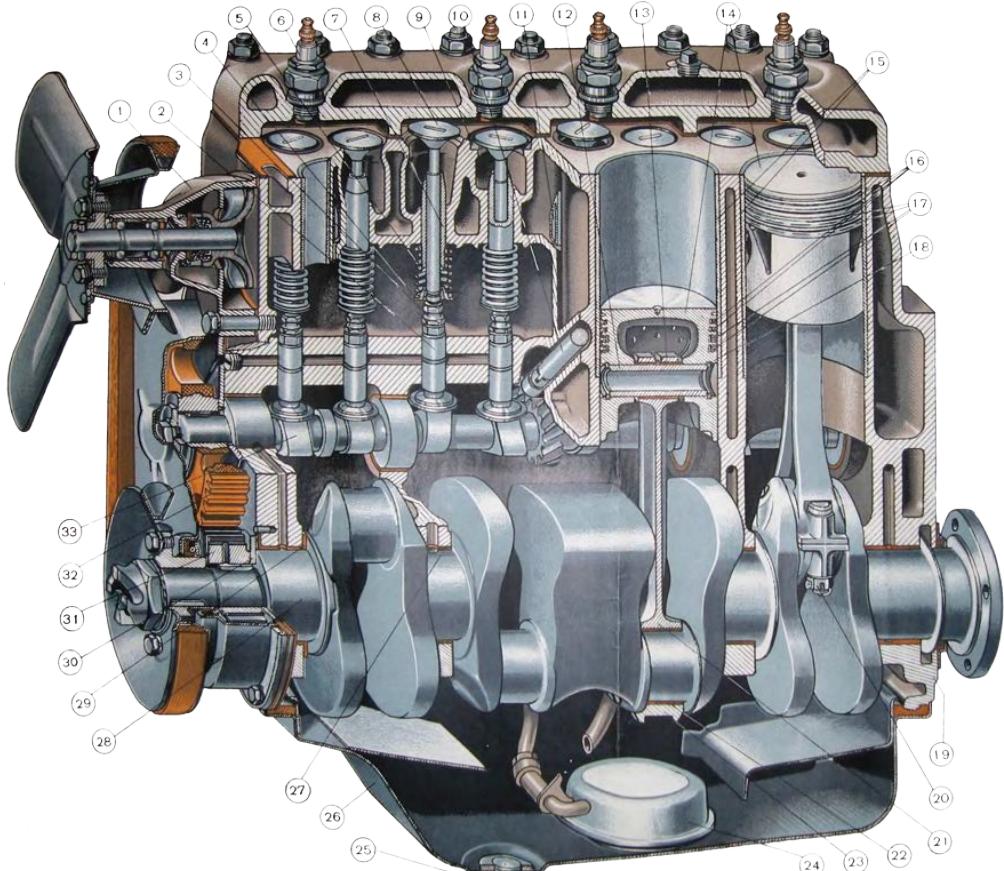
Двигатель автомобиля ГАЗ –М-20 с нижним расположением клапанов и распределительного вала: 1 – водяной насос, 2 – толкатель, 3- регулировочный болт толкателя, 4 – тарелка пружины, 5 – пружина клапана, 6 – запальная свеча, 7 – втулка клапана, 8 – выпускной клапан, 9 – жароупорное седло выпускного клапана, 10 – валик распределителя зажигания, 11 – водораспределительная труба, 12 – поршневой палец, 13 – втулка шатуна, 14 – поршень, 15 – гильза цилиндра, 16 – компрессионное кольцо, 17 – маслосъемное кольцо, 18 – спорное кольцо, 19 – крышка заднего коренного подшипника, 20 – гайка шатуна, 21 – шатун, 22- вкладыши шатуна, 23 – крышка шатуна, 24 – маслоприемник, 25 – пробка для слива масла из двигателя, 26 – масленый поддон, 27 – вкладыши коренного подшипника, 28 – коленчатый вал, 29 – упорное кольцо подшипника, 30 – упорная шайба коленчатого вала, 31 – шестерня коленчатого вала, 32 – шестерня распределительного вала, 33 – распределительный вал
